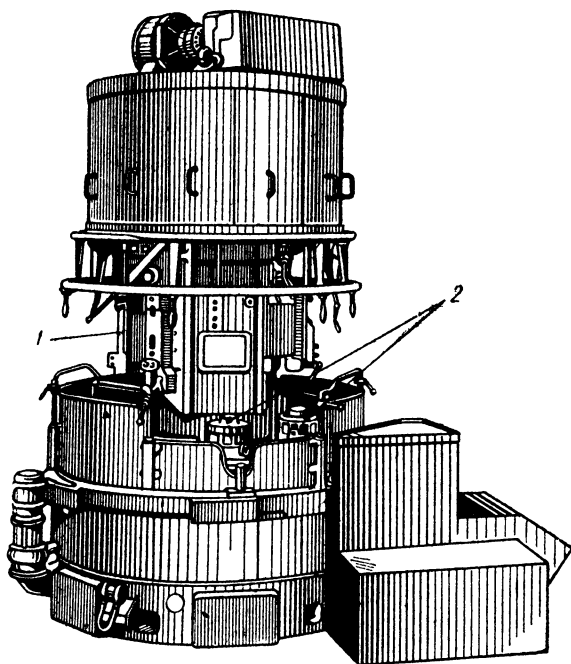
Вертикальный токарный шестишпиндельный полуавтомат модели 1 А 283.
